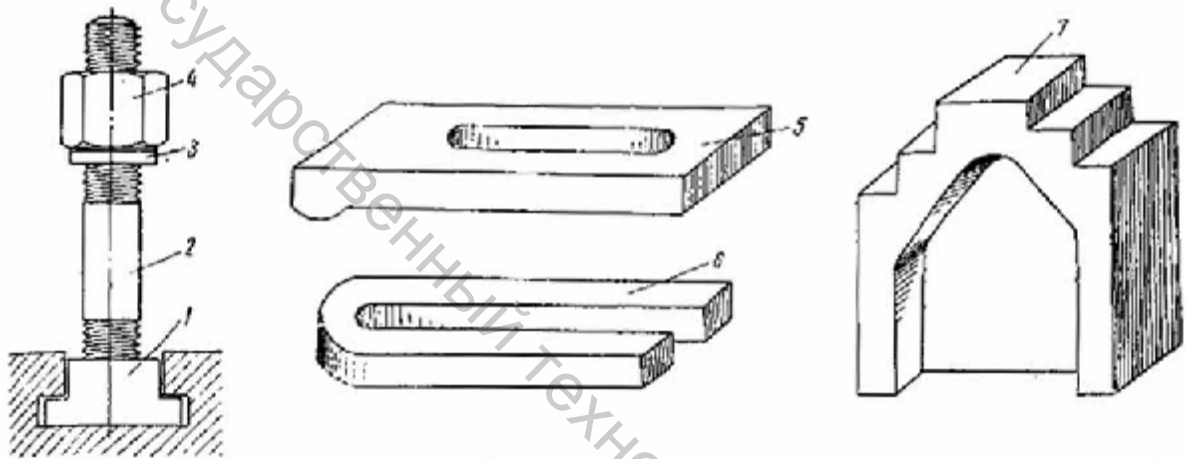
Крепежный комплект для закрепления обрабатываемых деталей
